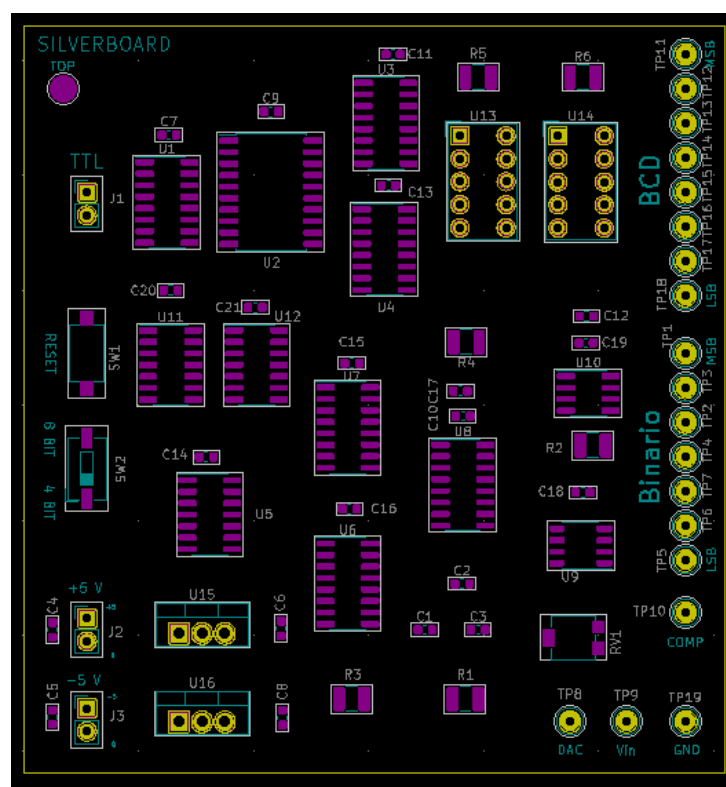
Colocación de componentes en la PCB con Pcbnew.
